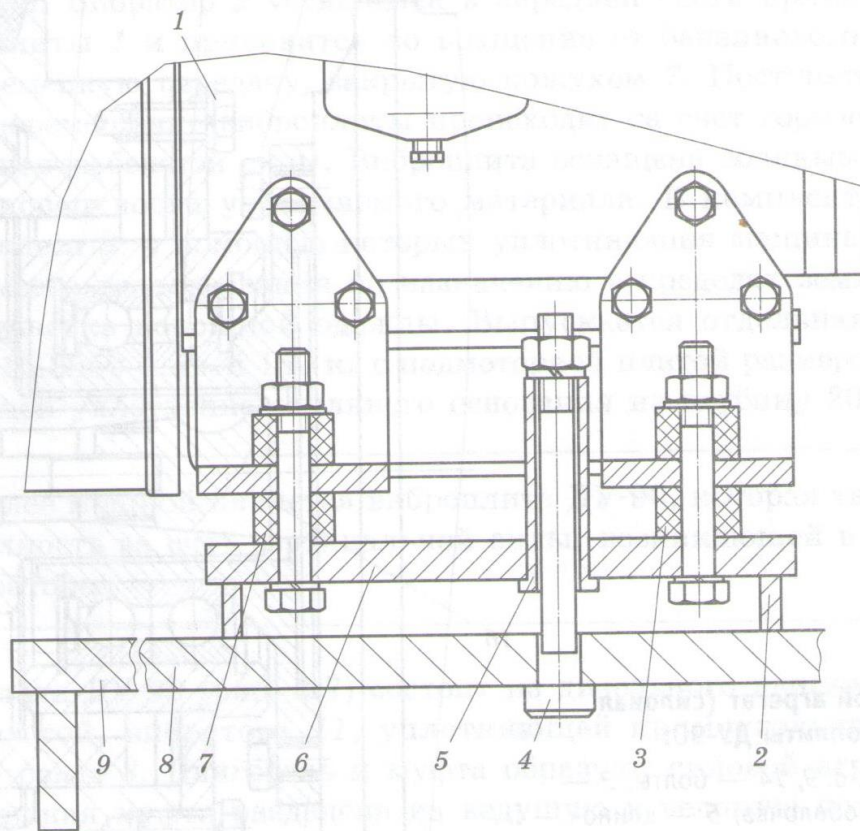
Крепление двигателя к раме уплотняющей плиты ДУ-90 через амортизаторы:
